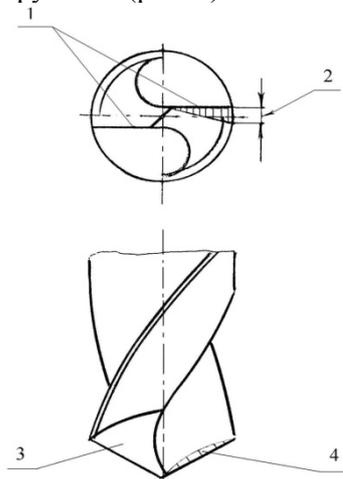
Схема определения износа рабочей части спирального сверла: 1 – режущая кромка; 2 – износ задней поверхности режущей кромки; 3 – задняя поверхность; 4 – износ по передней поверхности режущей кромки
